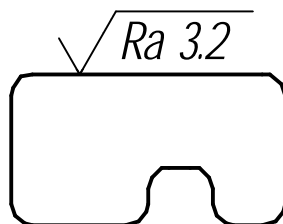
Обозначение одинаковой шероховатости поверхностей, образующих контур и плавно переходящих одна в другую
